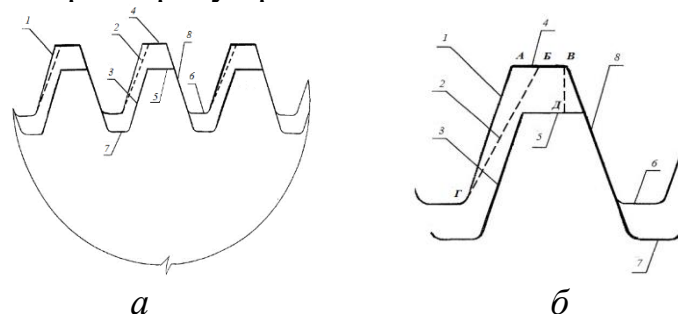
Відновлення профілю зношеної зубчастої частини крупногабаритного колеса: 1 – контур профілю робочої частини зуба колеса в первісному стані; 2 – границя зносу профілю робочої частини зуба шестерні, після визначеного терміну експлуатації; 3 – контур профілю робочої частини зуба колеса у відновленому стані; 4 – поверхня виступу зуба шестерні в первісному стані; 5 – поверхня виступу зуба шестерні у відновленому стані; 6 – поверхня впадини зуба колеса в первісному стані; 7 – поверхня впадини зуба шестерні у відновленому стані; 8 – контур профілю неробочої частини зуба шестерні в первісному і відновленому станах; А–Г – границя поверхні профілю зуба шестерні в первісному стані; Б–Г – границя поверхні профілю зуба колеса при його зношенні в процесі експлуатації; А–Б – зона зношування поверхні виступу зуба колеса; В – зона поверхні виступу зуба шестерні в зношеному вигляді після експлуатації колеса; В–Д – висота зони видалення зношеної частини зуба колеса
